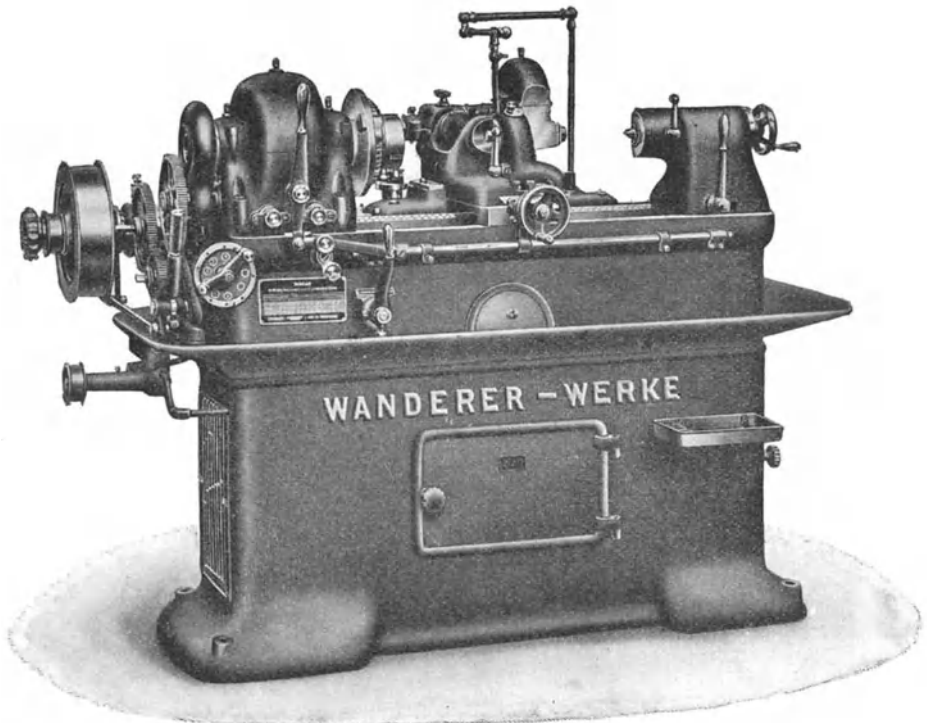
Die Gewindefräsmaschine von Wanderer.
